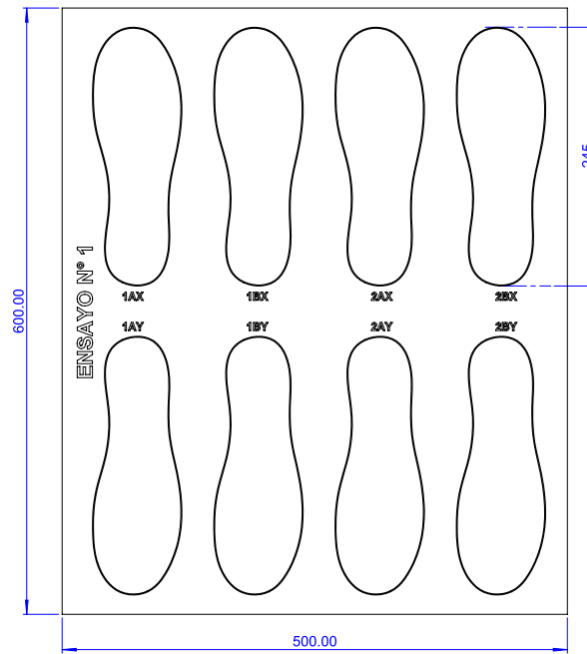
22. Dimensiones placa de ensayo N°. 1.
